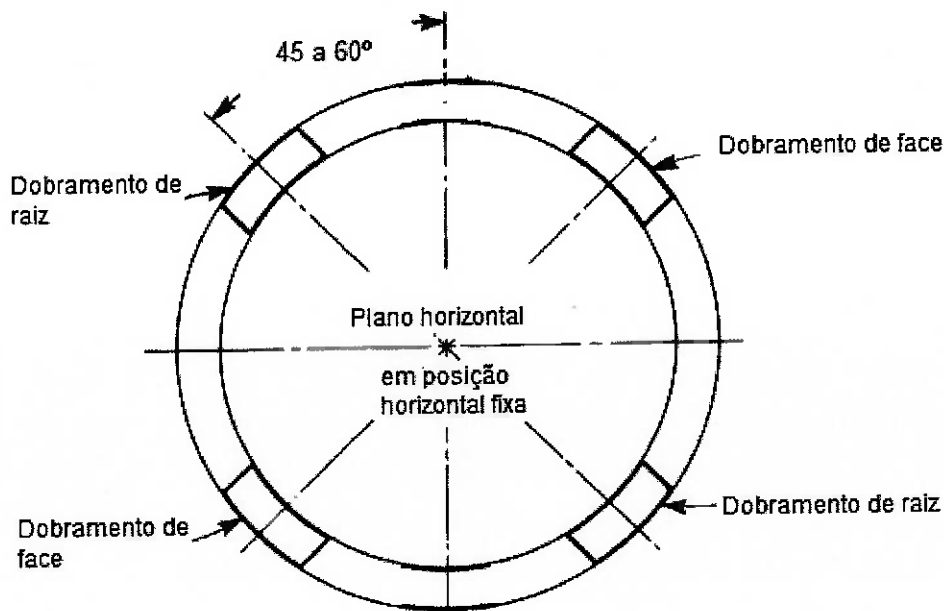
Locais para a retirada de corpos de prova para ensaios de qualificação de soldadores para juntas de topo, segundo a ASME IX, para espessuras de parede menores que 19 mm [11].
